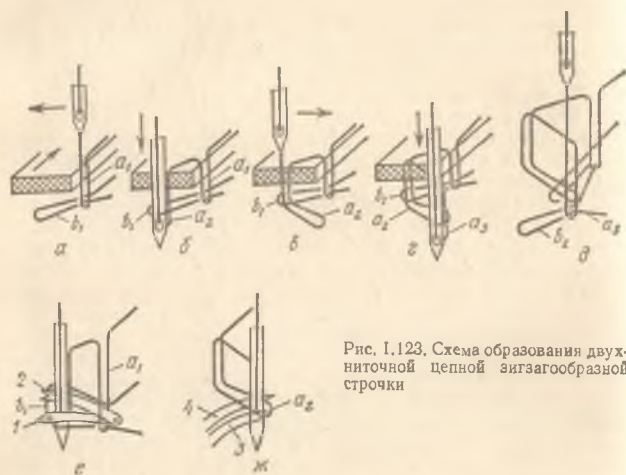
Схема образования двухниточной цепной зигзагообразной строчки
